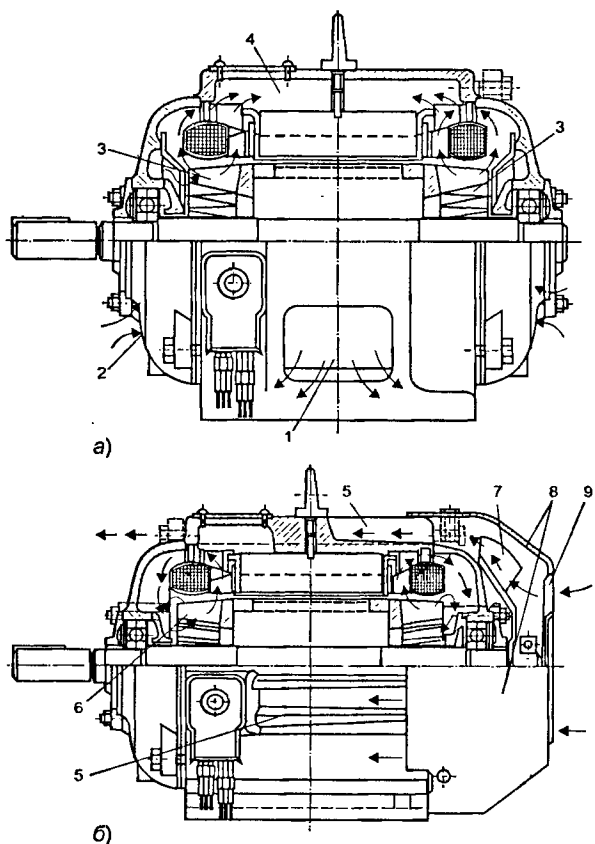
Разрез и схема движения охлаждающего воздуха асинхронных электродвигателей первой единой серии (4-й габарит): а — двигатель защищенного исполнения (А); б — двигатель закрытого обдуваемого исполнения (АО); 1 — отверстие в корпусе для выхода охлаждающего воздуха; 2 — отверстие в подшипниковых щитах для входа охлаждающего воздуха; 3 — лопатки; 4 — продольное ребро корпуса для крепления сердечника статора; 5 — наружные охлаждающие ребра корпуса; 6 — лопатки вентилятора, перемешивающие воздух внутри машины; 7 — вентилятор наружного обдува; 8 — кожух вентилятора наружного обдува; 9 — отверстие в кожухе для засасывания охлаждающего воздуха
